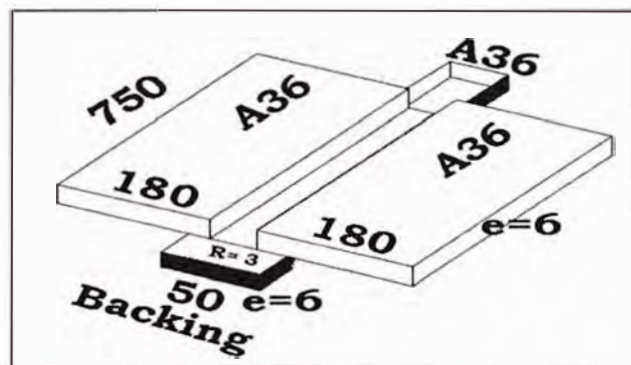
Cupón de soldadura para GMAW mecanizado
